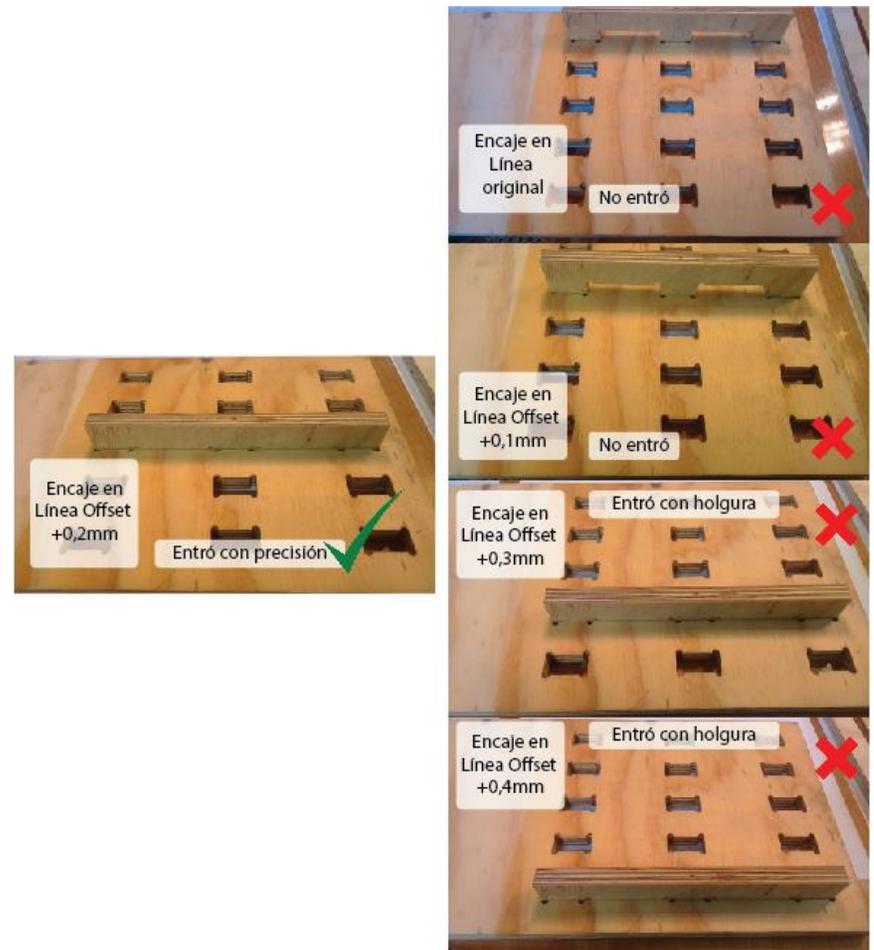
Validación de elementos y columnas de encaje. Fuente: Elaboración propia
